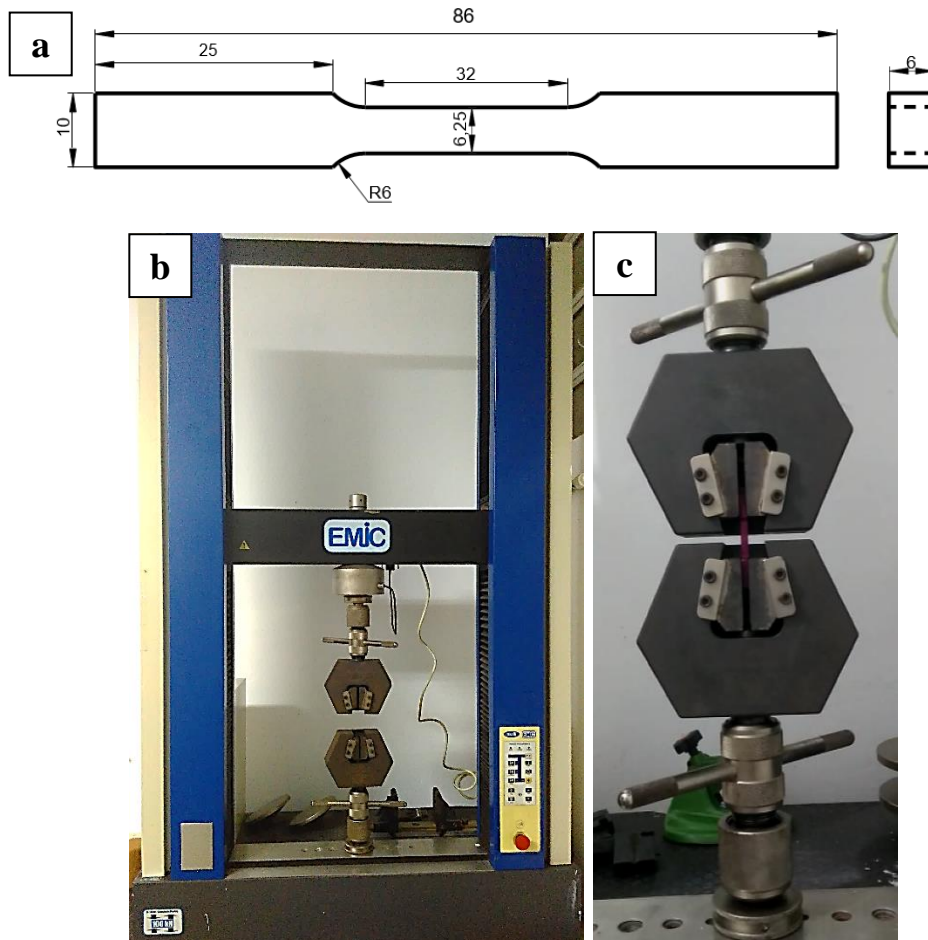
Ensaio de tração. (a) corpo de prova do ensaio de tração (medidas em mm); (b) e (c) máquina garras utilizadas no ensaio.
